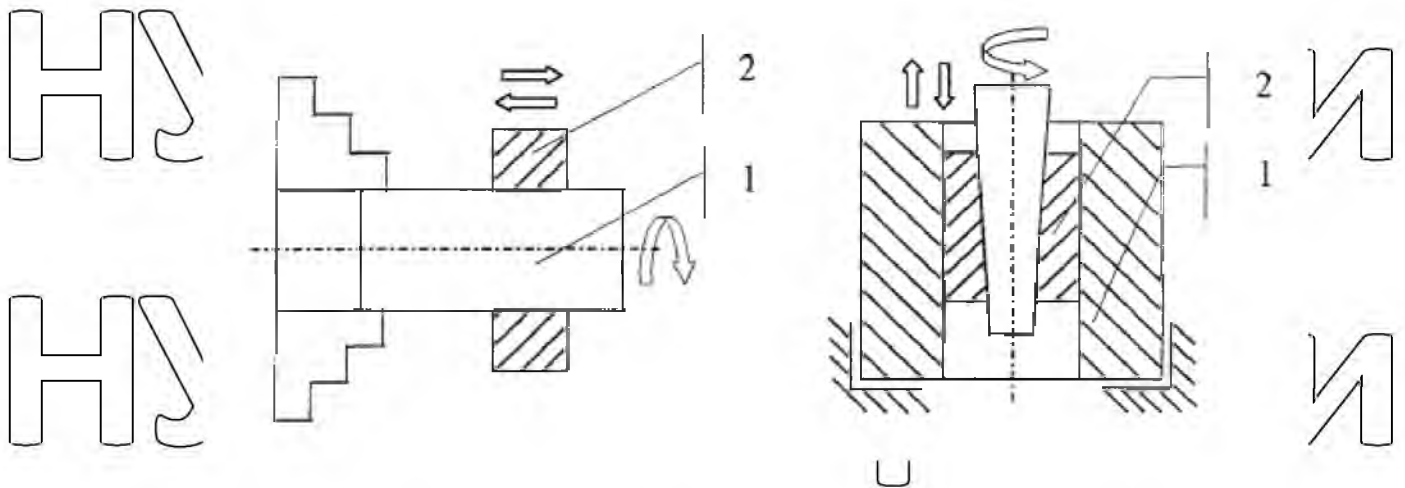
Схеми доведення деталей з'єднання «золотник-корпус»: 1 - деталь, 2 - притир.
